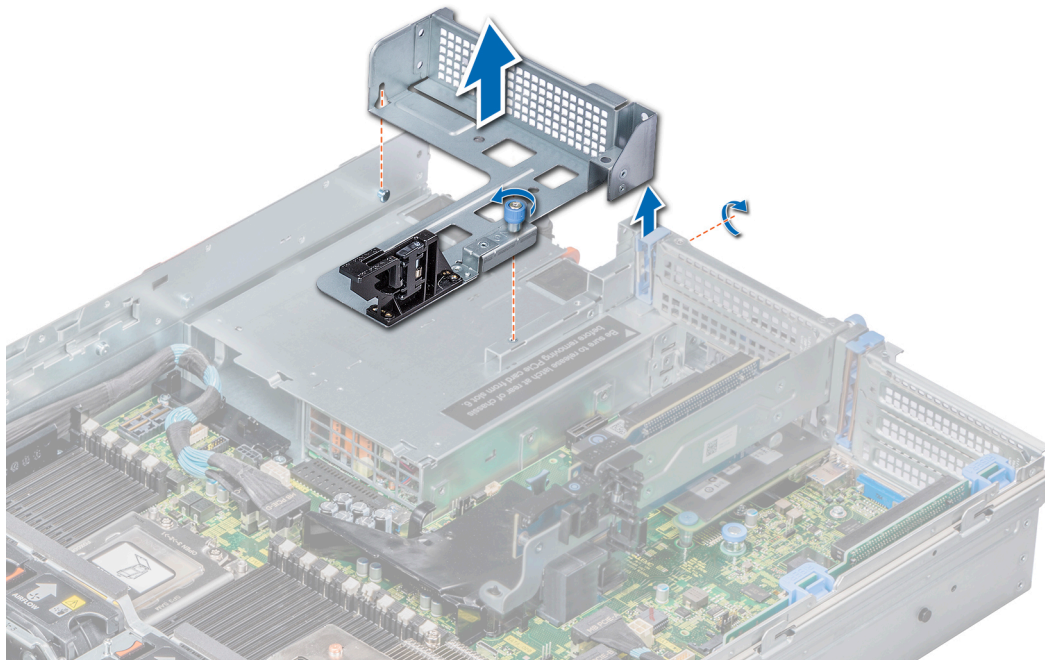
Entfernen der Platzhalterkarte für Riser 3
